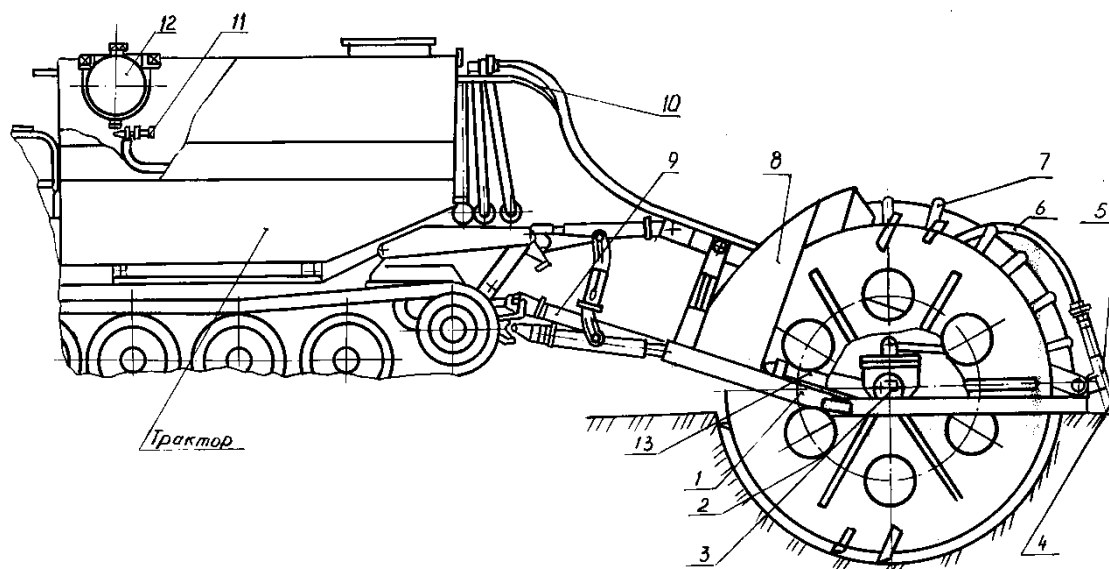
Схема лесопожарного агрегата в составе трактора ТЛП-4 с орудием заградительным торфяным ОЗТ-0,9: 1 – рама; 2 – фреза; 3 – редуктор привода фрезы; 4 – ствол воздушно-пенный СВП-М модернизированный для работы с кислотой; 5 – кронштейн крепления ствола; 6 – рукав напорный; 7 – защитная пластина; 8 – кожух фрезы; 9 – вал карданный; 10 – рукав кислотный; 11 – кран подачи кислоты; 12 – бак для кислоты; 13 – опора технологическая
